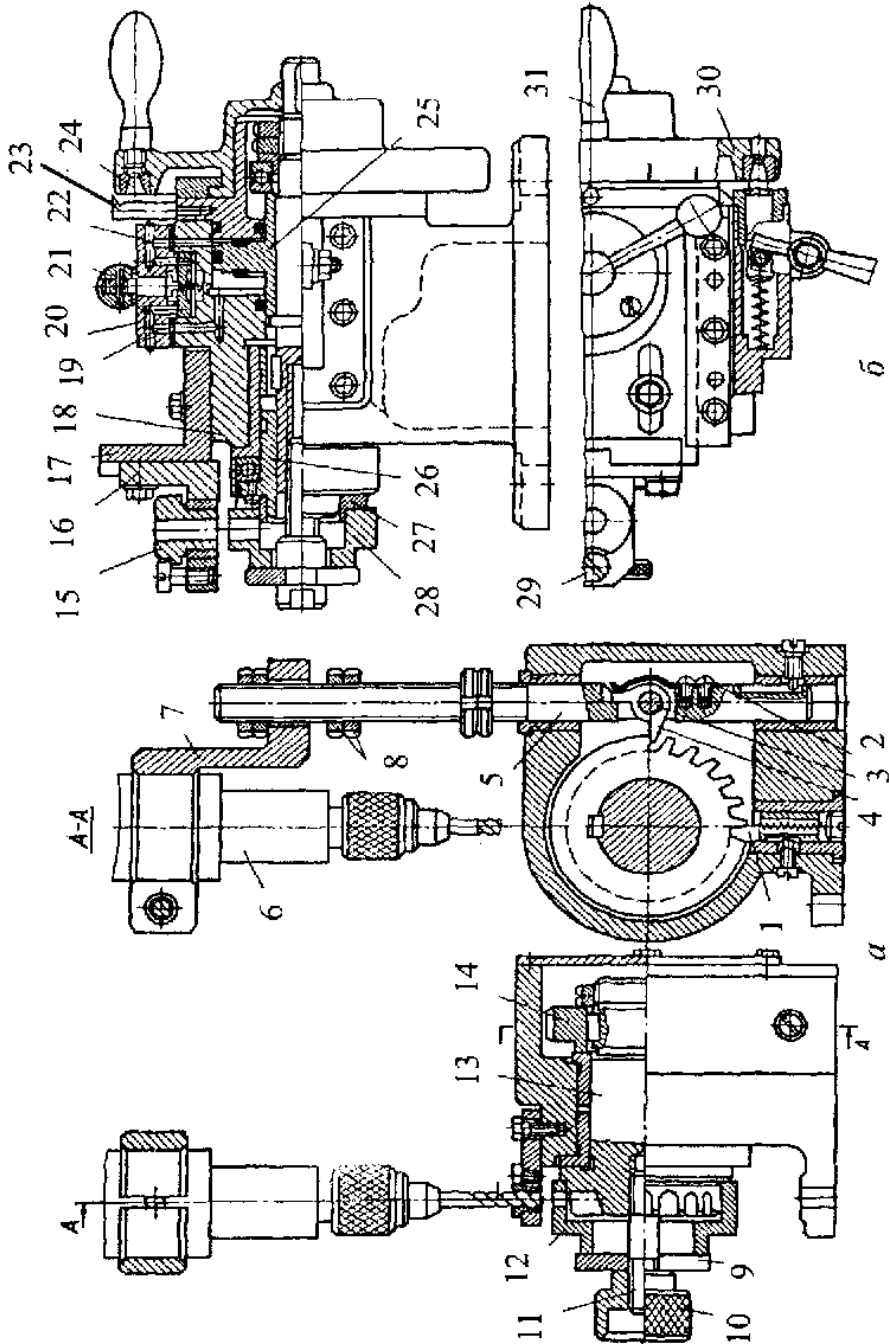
Схема поворотного пристрою для дрібних деталей
